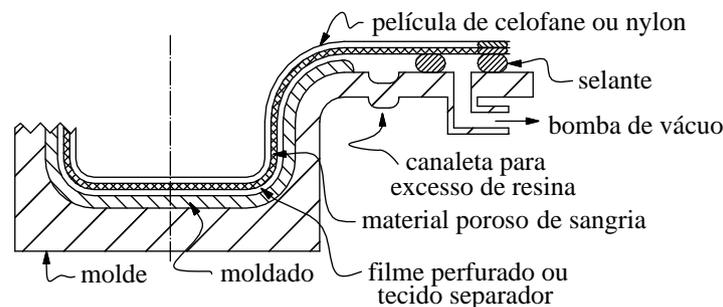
Esboço dos principais componentes do processo de moldagem por membrana a vácuo.
